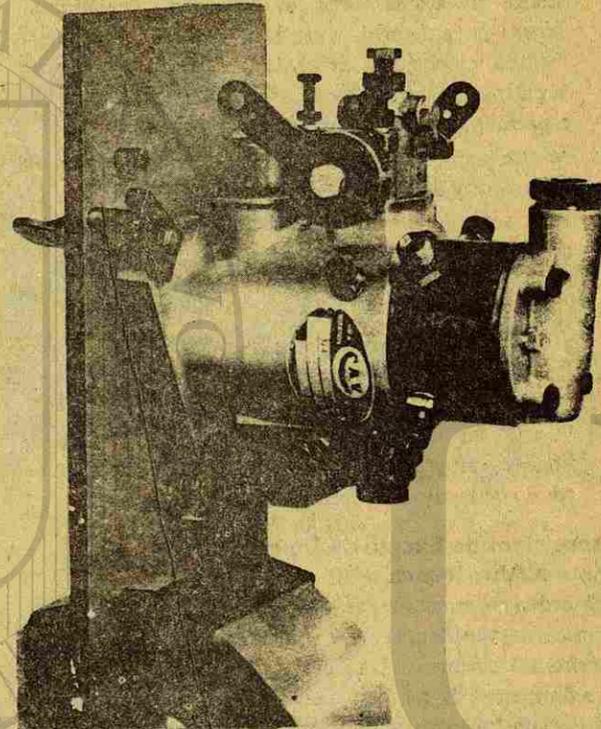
Regulador hidráulico de montaje reversible, puesto en el dispositivo de montaje y desmontaje
